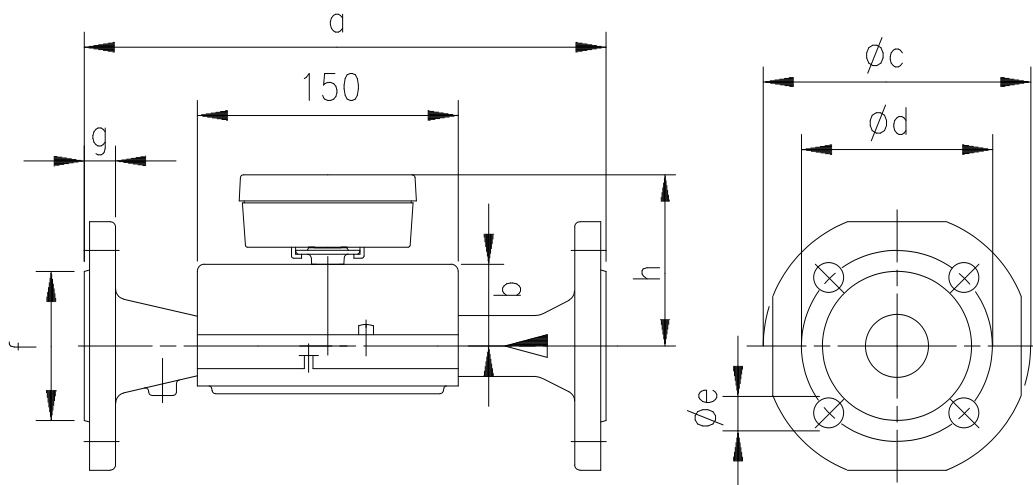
Габаритные и установочные размеры преобразователей расхода исполнений:
